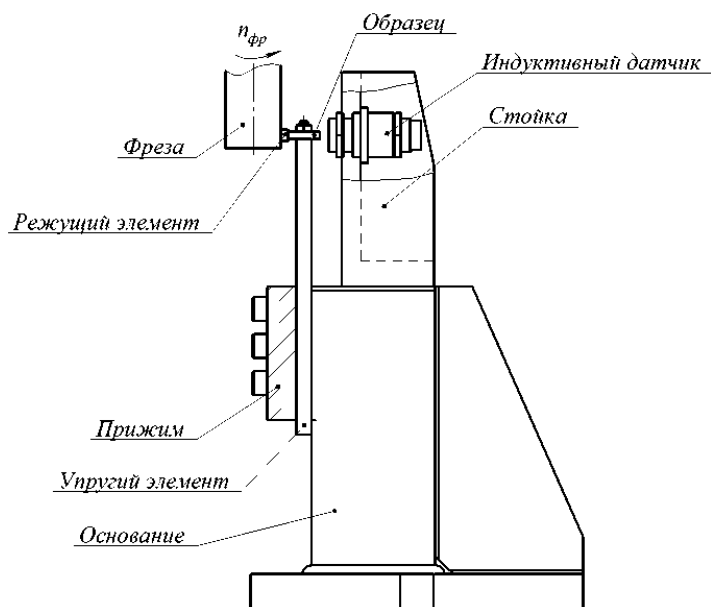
Схема стенда для исследования механических колебаний при фрезеровании тонкостенных деталей
